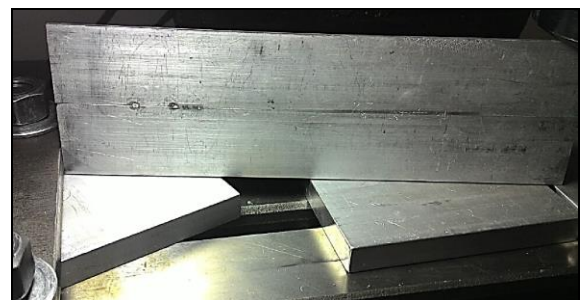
Raiz das chapas de alumínio 6063T6 unidas pelo processo FSW utilizando ferramental cilíndrico.
